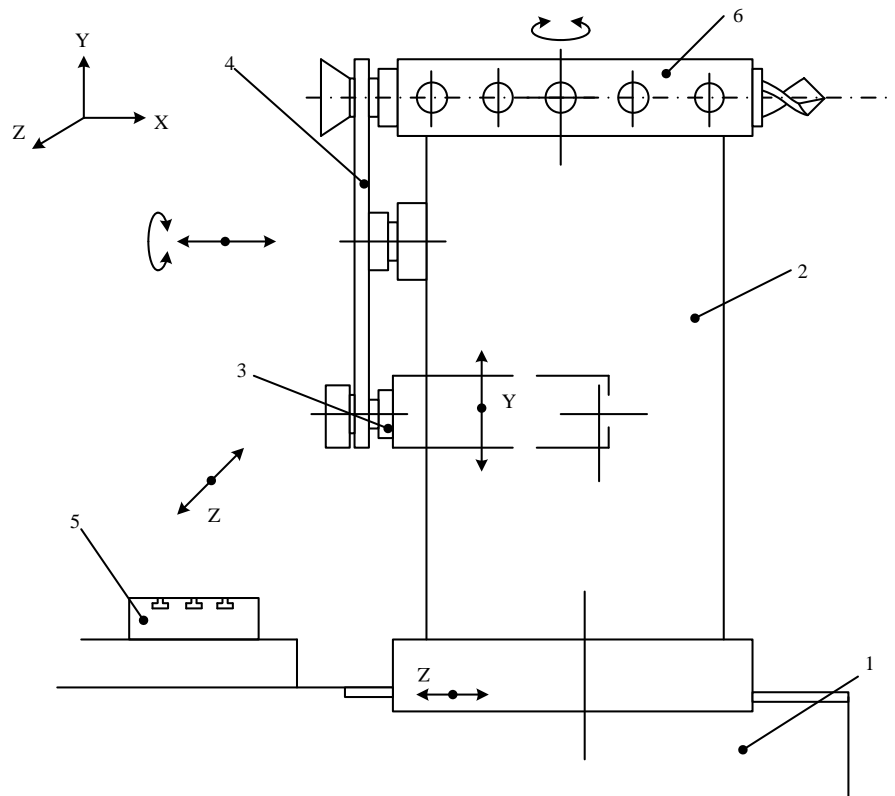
Компонівка багатоопераційного верстату з верхнім діленням інструментального магазину
